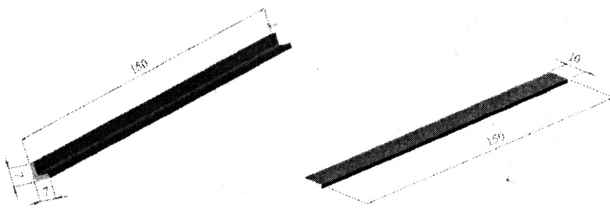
Внешний вид образцов из труб, подвергнутых испытаниям: 1 — образец, вырезанный из зоны изгиба прямоугольной трубы, 2 — образец, вырезанный из боковой стенки трубы
